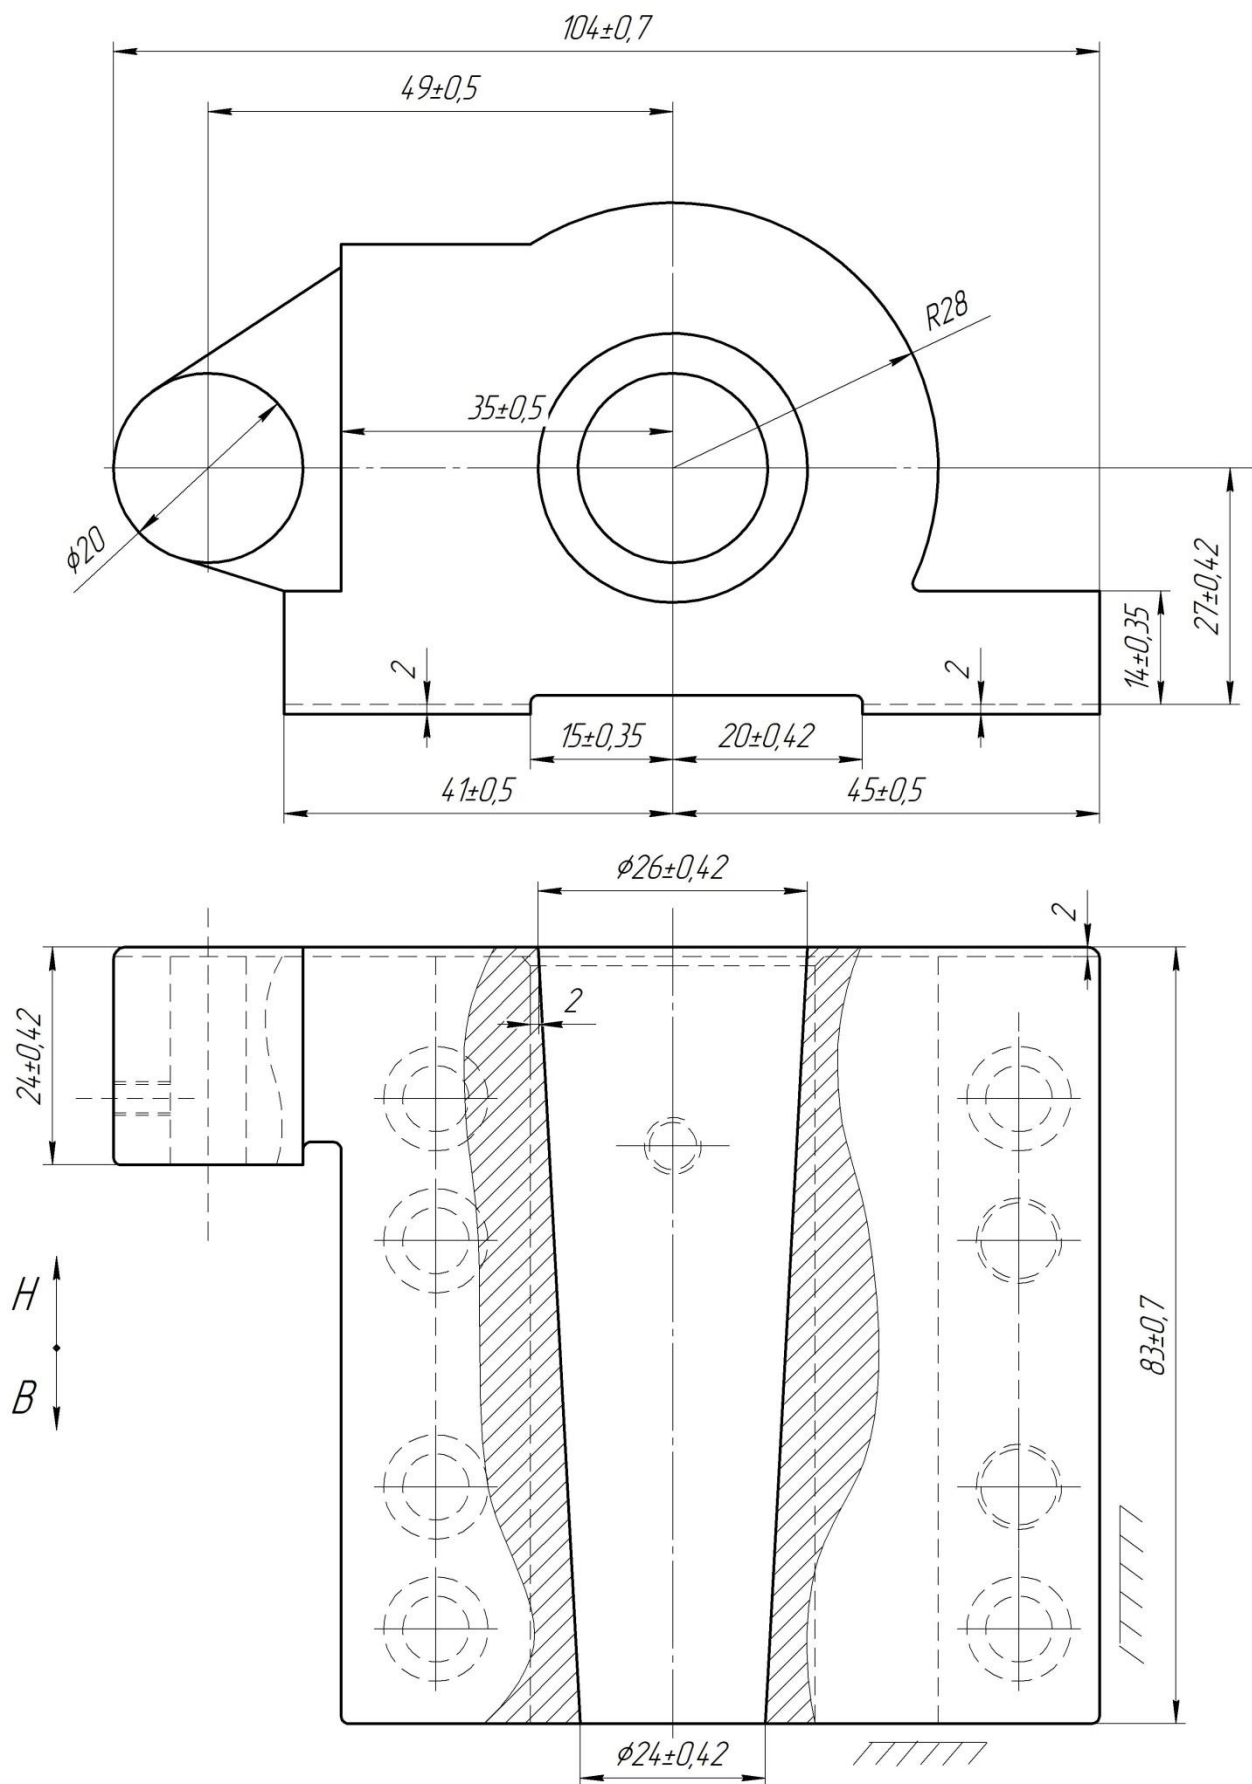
Общий вид заготовки - «Кронштейна»
